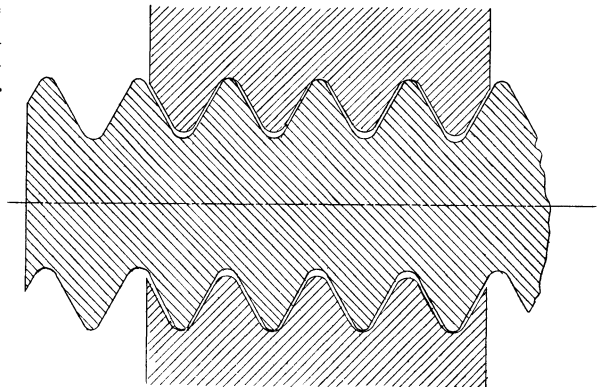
Gewinde mit zu schwachem Flankenmaß.
